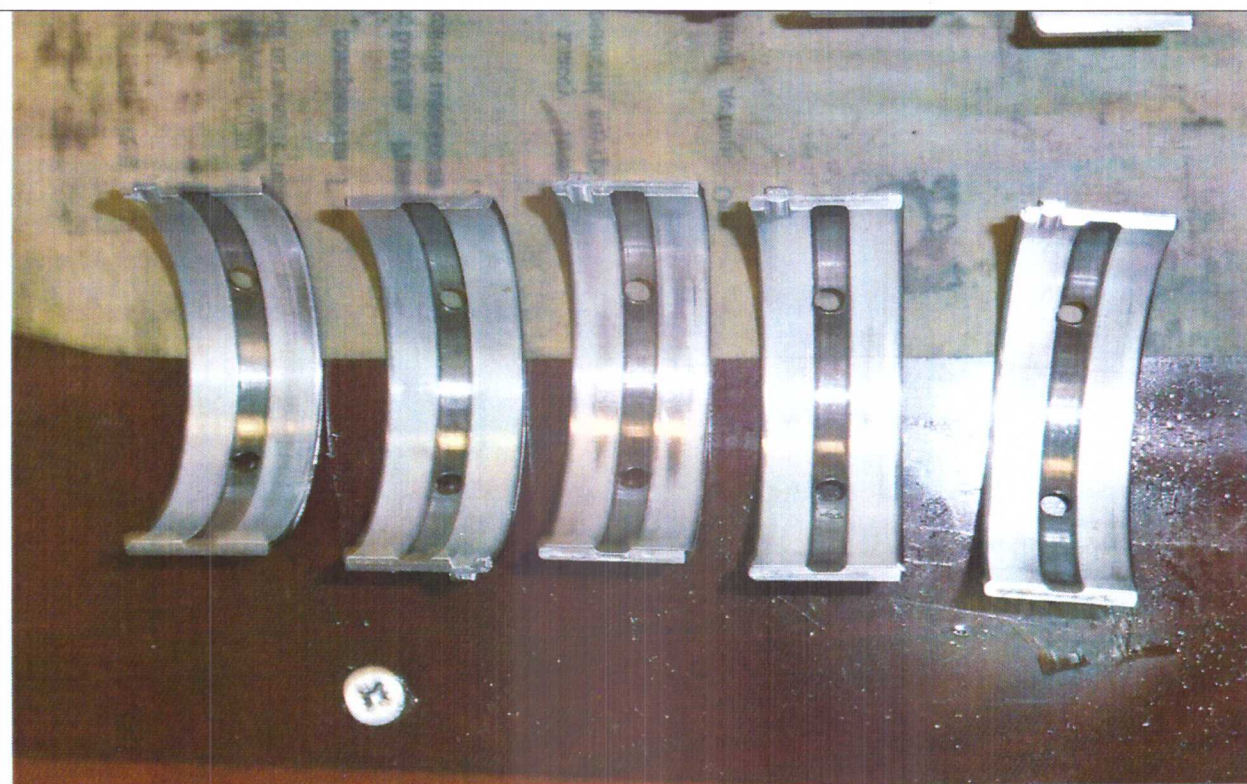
Внешний вид рабочей поверхности верхних вкладышей коренных подшипников коленчатого вала по окончании длительных испытаний двигателя при работе на базовом масле Castrol EDGE с добавкой нанокompозита Amortect PROOF
